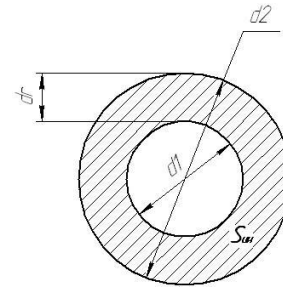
Изображение торца кольцевого сварочного инструмента
